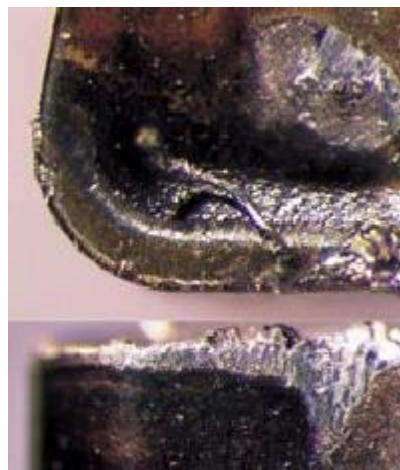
Desgaste de flanco na ferramenta de metal duro TNMG 160408-23 classe S15 (GC1105) na usinagem da liga de níquel Inconel 718 - $V_c = 90$ m/min., $f = 0,15$ mm/rot. e $a_p = 0,8$ mm.
